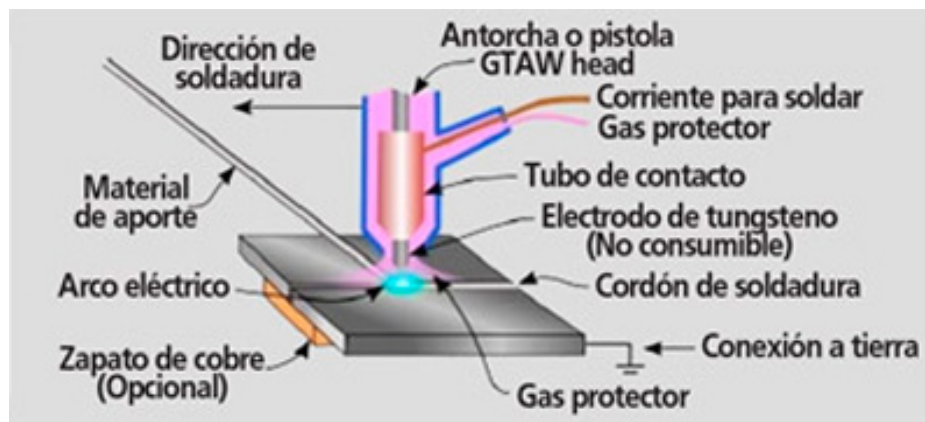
Esquema del proceso en la soldadura TIG. [12]
